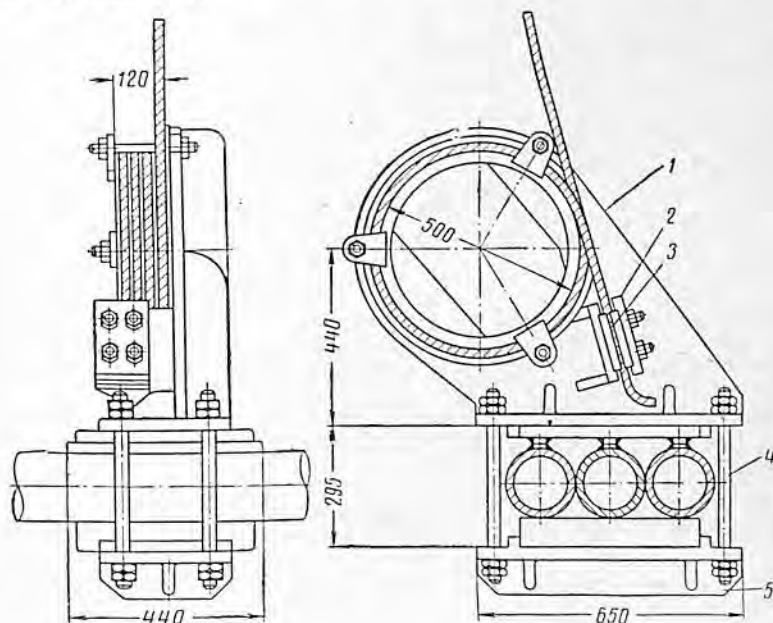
Приспособление для крепления неподвижного конца талевого каната.
